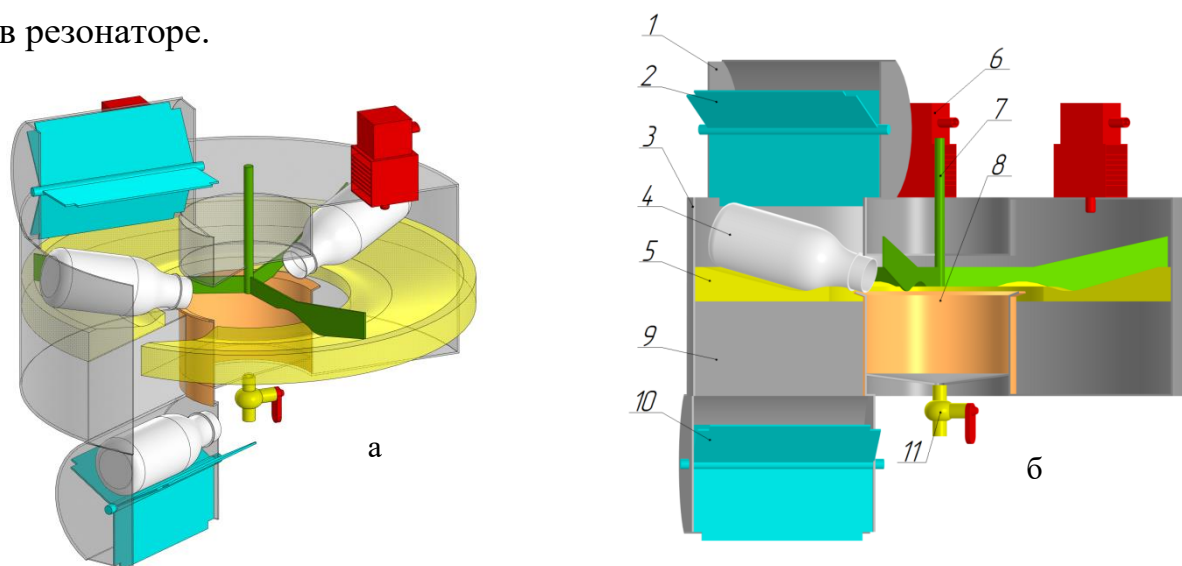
СВЧ-размораживатель молозива животных непрерывно-поточного действия с тороидальным резонатором: а) общий вид; б) общий вид с позициями; 1 – шлюзовой затвор; 2 – отсеки роторного питателя; 3 – тороидальный резонатор; 4 – молозиво в пластиковой бутылке; 5 – диэлектрическая наклонная платформа; 6 – волновод, магнетрон и вентилятор; 7 – ротор с диэлектрическими лопастями с электроприводом; 8 – керамический цилиндр в конденсаторной части резонатора; 9 – тороидальная часть резонатора; 10 – шлюзовой затвор; 11 – шаровой кран в запредельном волноводе
